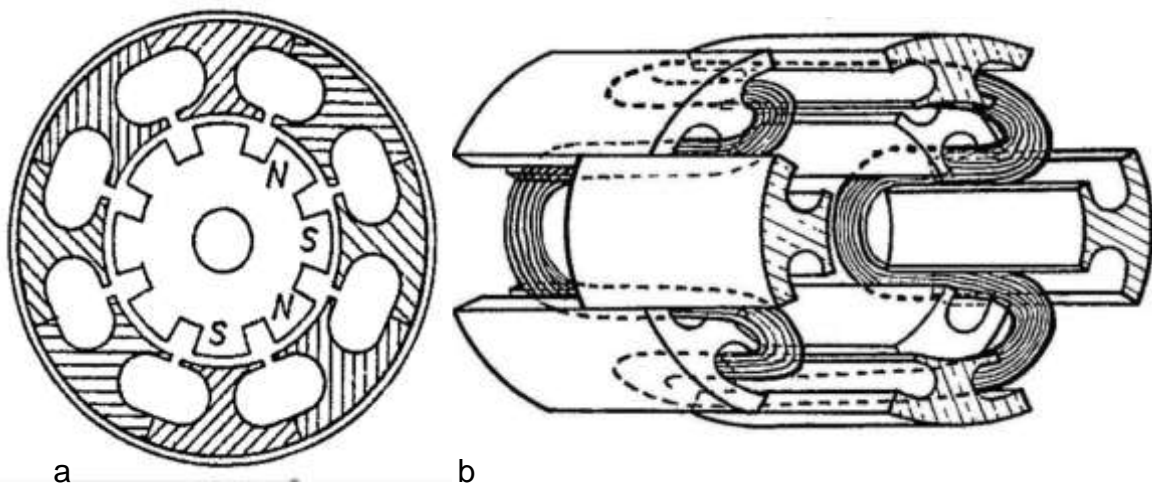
Zeichnungen im englischen Patent Nr. 615331, a) Querschnitt ohne Wicklung, b) Zusammenfügen der Ankereisenelemente mit der Spule
